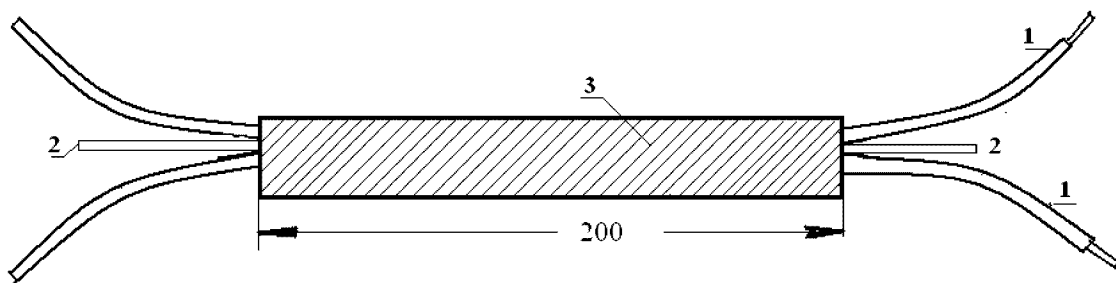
Образец провода круглого сечения диаметром более 2,50 мм или прямоугольного сечения для испытания высоким напряжением:
